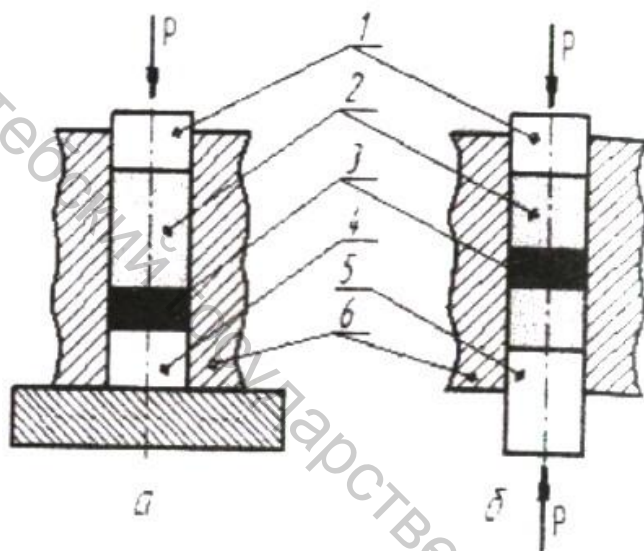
Схемы одно-(а) и двустороннего (б) прессования порошков: 1 – подвижный верхний пуансон, 2 – порошок, 3 – спрессованная заготовка, 4 – неподвижный пуансон, 5 – подвижный нижний пуансон, 6 – матрица
